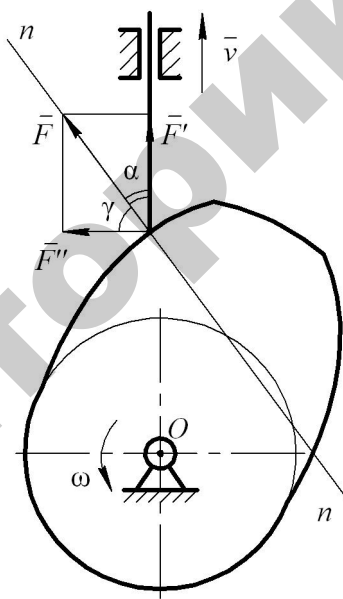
Схема к определению сил, действующих в высшей кинематической паре кулачкового механизма
